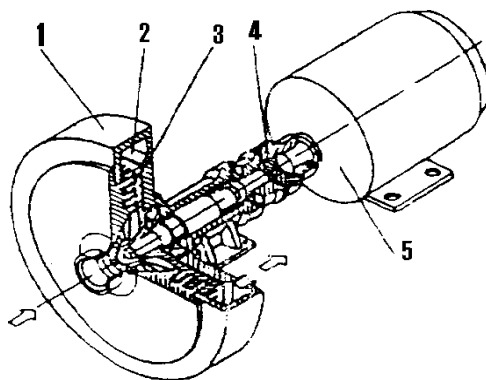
Загальний вид зубчастого гомогенізатора: 1 – корпус; 2 – гомогенізуюча головка; 3 – ротор; 4 – муфта; 5 – електродвигун
